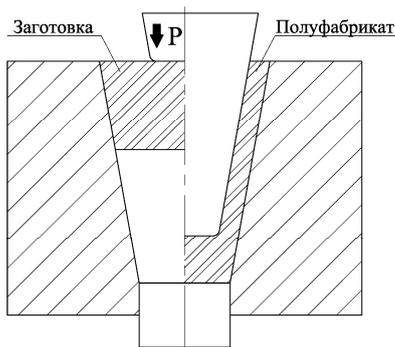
Исходная заготовка и схема процесса получения полой конической детали
